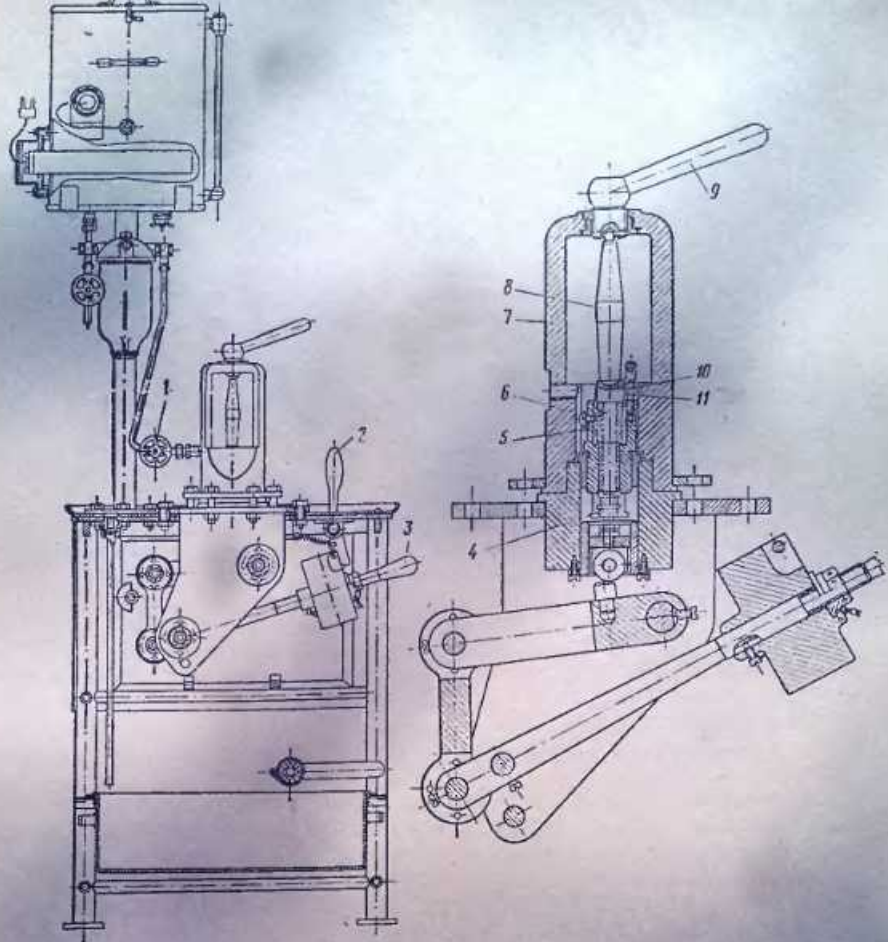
Установка ЛМ9690-190 для опрессовки пары плунжер — втулка
